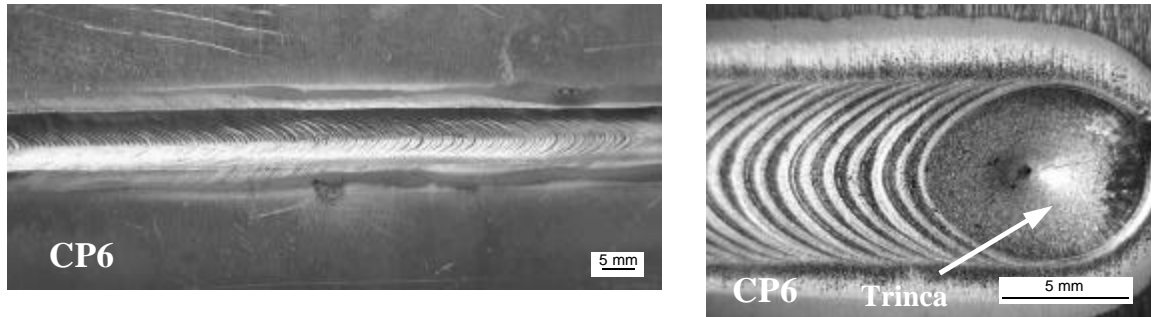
Solda com  $I_p$  220A e  $I_b$  110A, 6 pulsos/s, com suporte de cobre no reverso.
